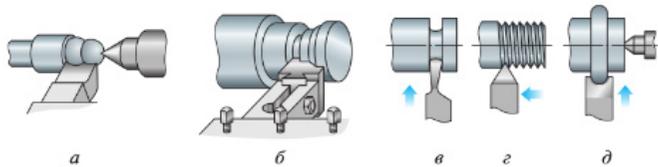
Фасонные резцы: а — цельный; б — с механическим креплением режущей кромки; специальные фасонные резцы: в — галтельный; г — резьбовой; д — фасонный для обработки бурта
